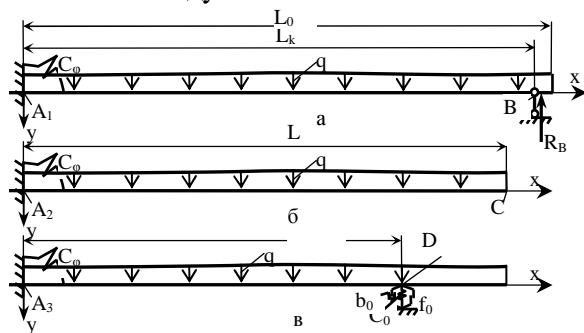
Зміна умов опирання і закріплення заготовки, яка має місце при роботі верстата: а – опирання кінцевої частини заготовки на кільце; б – консольне закріплення заготовки; в – введення проміжної пружно-демпфуючої опори заготовки
